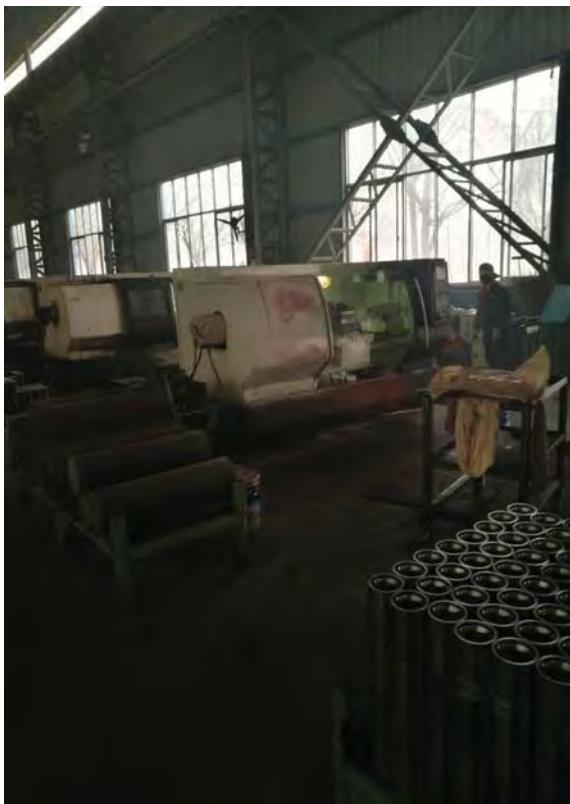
减速机齿轮及齿轮轴工艺的数控车床 图 2-25 减速机齿轮及齿轮轴工艺滚齿成型（滚齿机）
